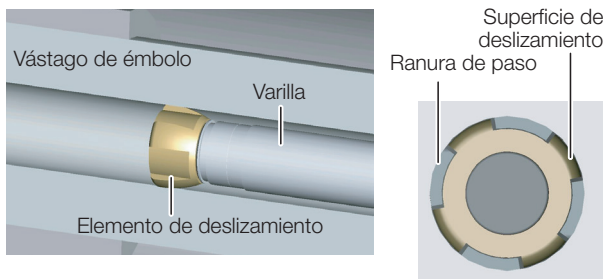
Vista detallada y vista desde arriba del elemento de deslizamiento
